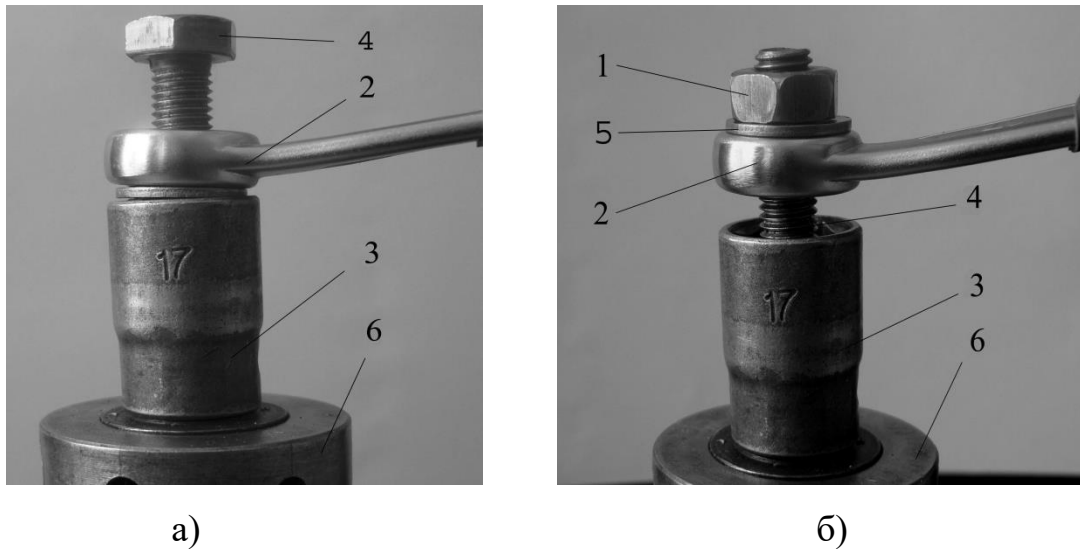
Схеми встановлення досліджуваних деталей у торцевій головці на торсіонному тензометричному валу: а) процес законтрування гайок, б) процес скручування імітатора шпильки: 1 – контргайка; 2 – кільцевий ключ; 3 – торцева головка; 4 – болт; 5 – шайба; 6 – торсіонний тензометричний вал.
